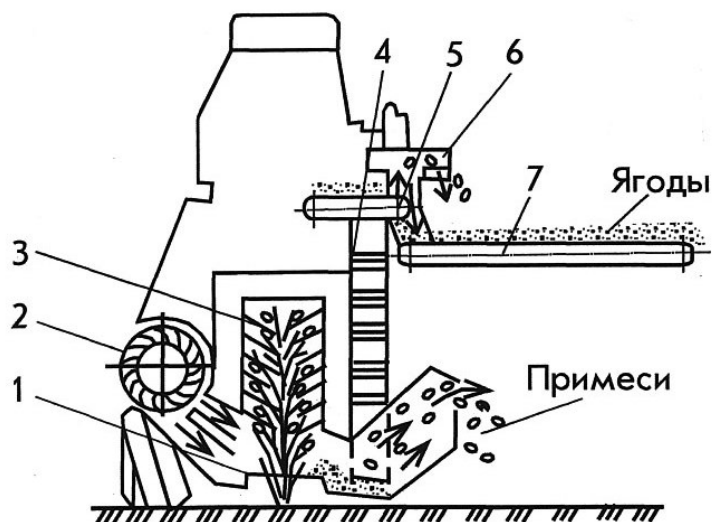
Схема рабочего процесса ягодоуборочной машины пальцевого типа: 1 – пальцы; 2 – вентилятор; 3 – дополнительный улавливатель; 4 – основной улавливатель; 5, 7 – транспортеры; 6 – направляющий воздушного потока
